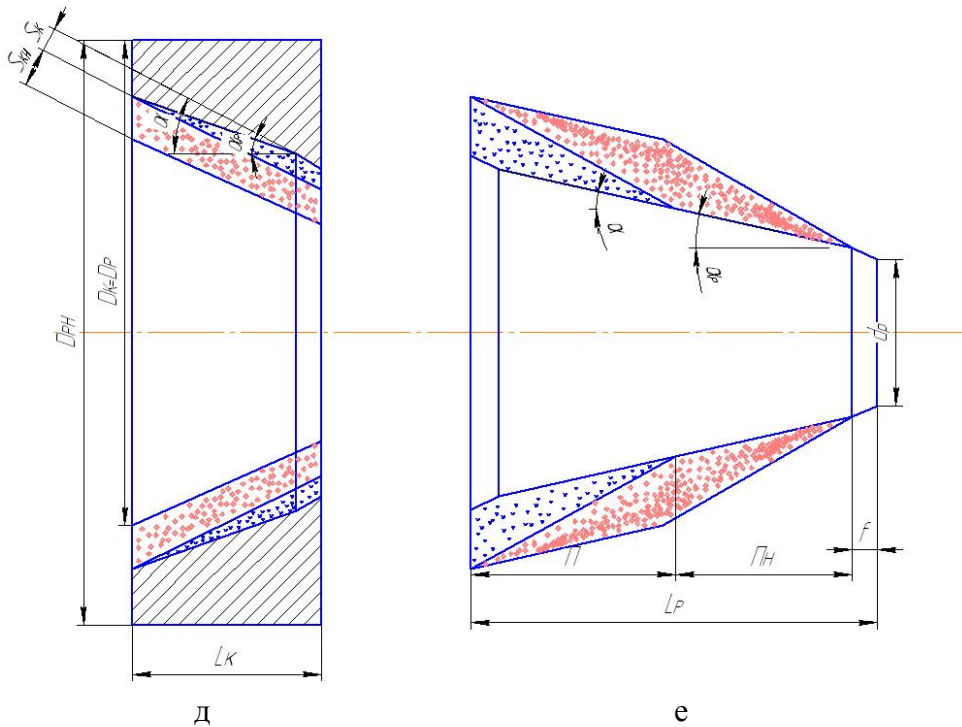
Схема сопряжения рабочих конических поверхностей ротора и корпуса установки Камюр
